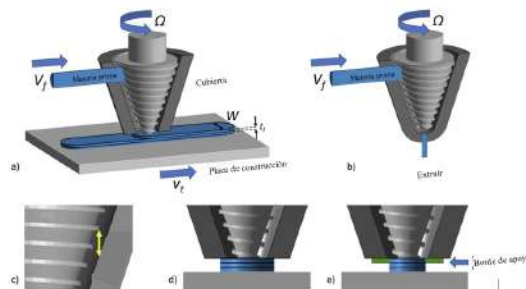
Proceso de fabricación aditiva de extrusión por tornillo de fricción [24].
